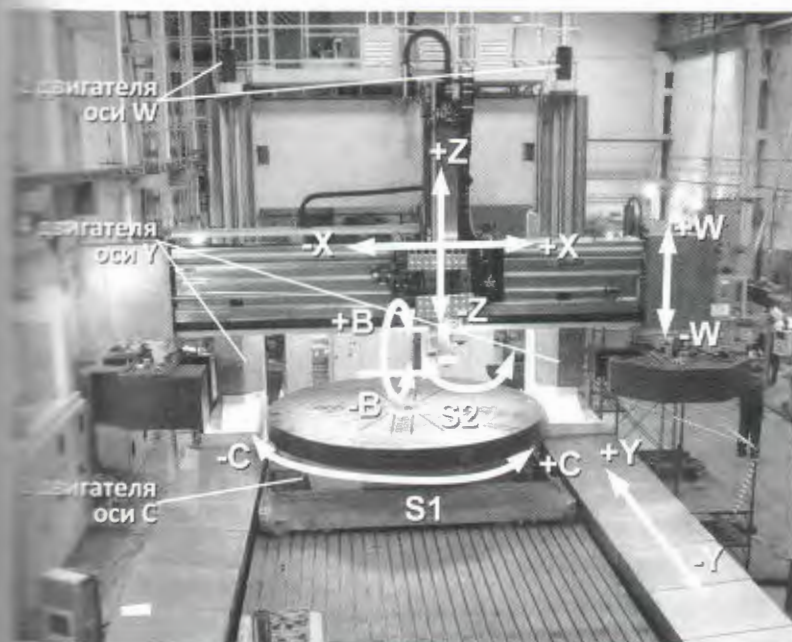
Внешний вид и кинематическая схема станка VMG50
